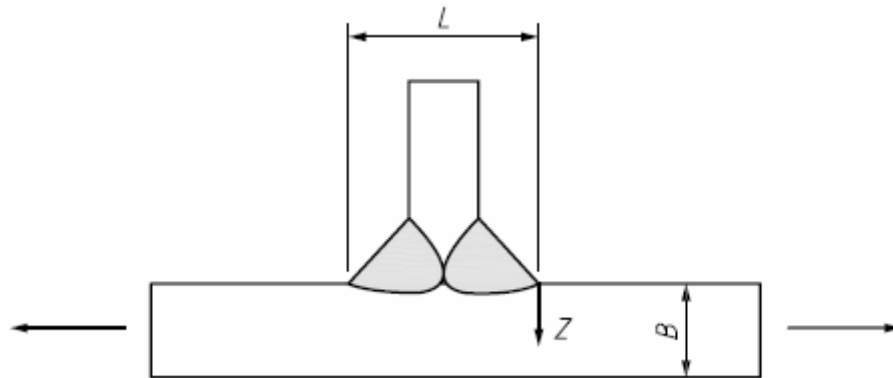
Representação da geometria do cordão de soldadura presente na zona central do corpo da caixa [2].
